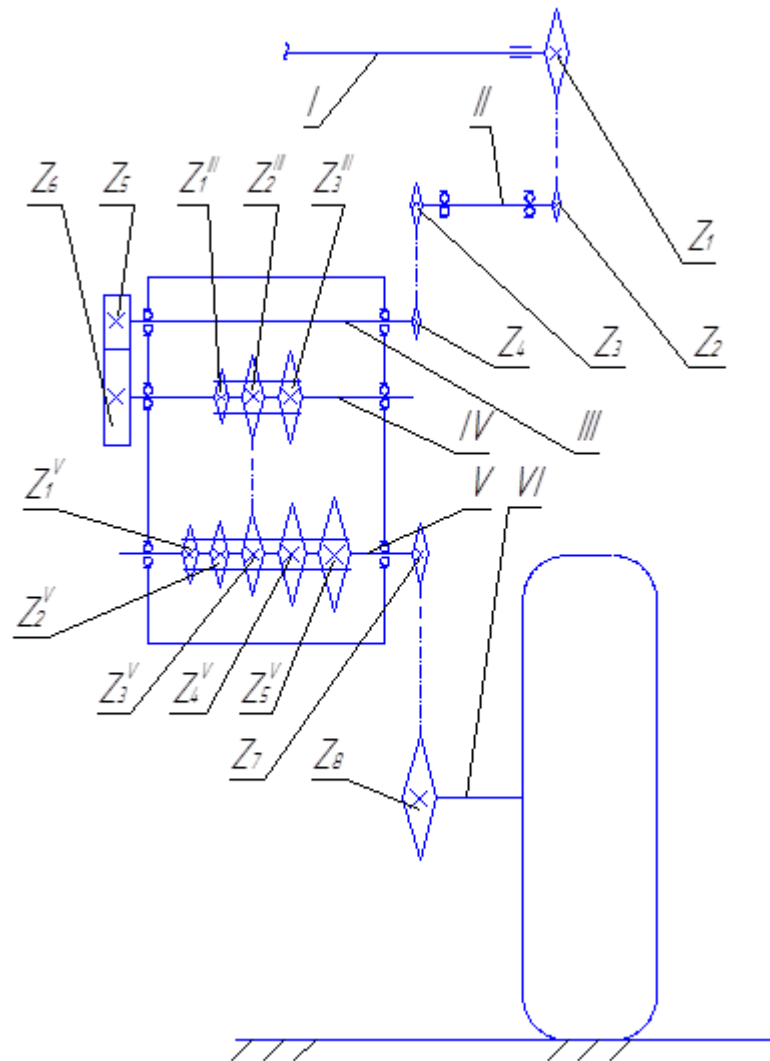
Схема приводу висіваючих апаратів: *I* – вал висіваючих апаратів; *II* – проміжний вал; *III* – вихідний вал касети; *IV* – вихідний вал коробки зміни передач; *V* – вхідний вал коробки зміни передач; *VI* – вал опорно-приводного колеса.
